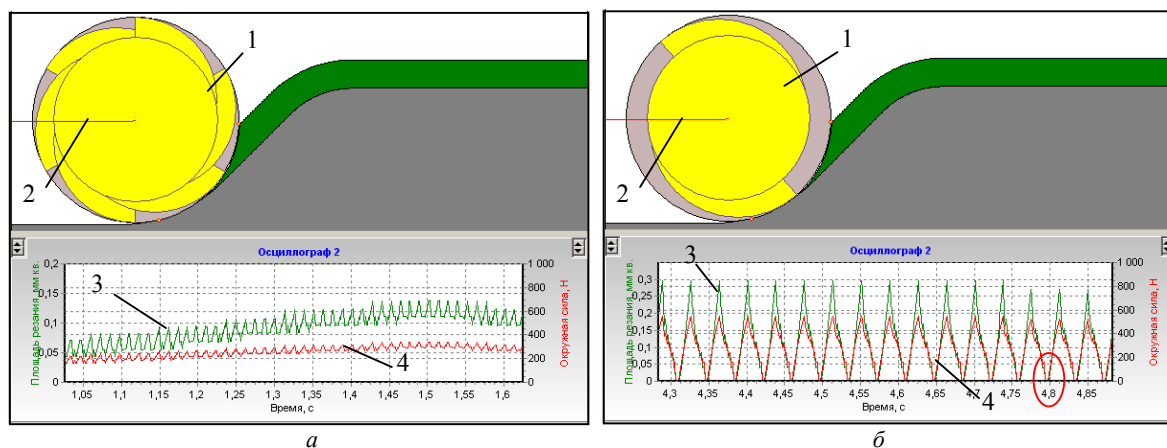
Осцилограми фрезерування контуру: а – фрезою  $z=6$ , б – фрезою  $z=2$
